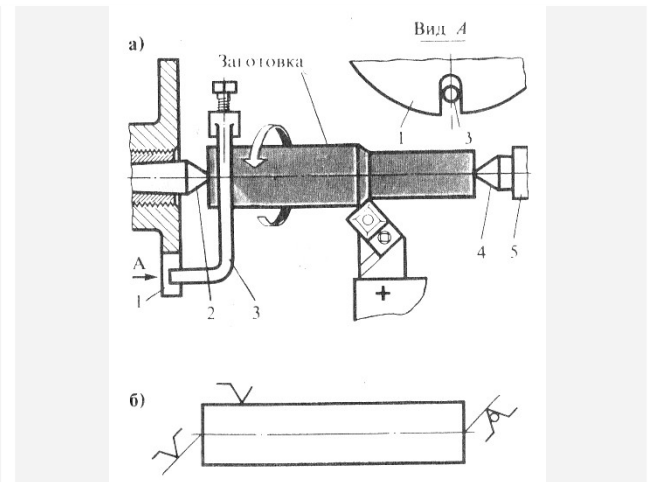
Установка заготовки в центрах (а), условная схема (б). Технологические базы - конические поверхности центровых отверстий в торцах вала.
